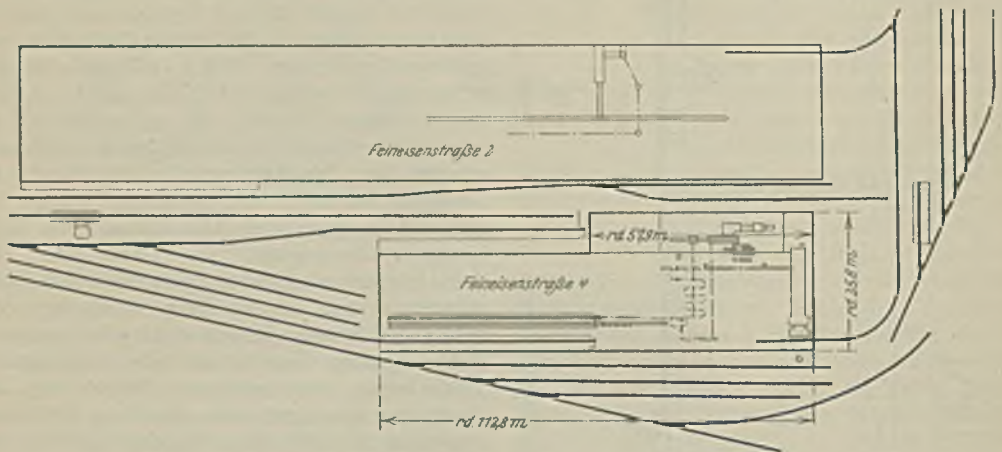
Lageplan der neuen Feineisenstraße der Wisconsin Steel Company.
